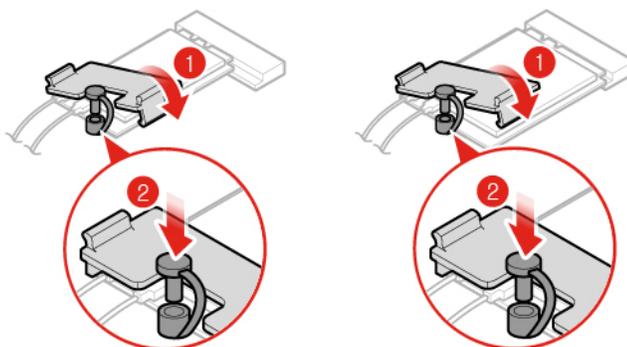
Installazione della protezione della scheda Wi-Fi (tipo 1 e 2)
